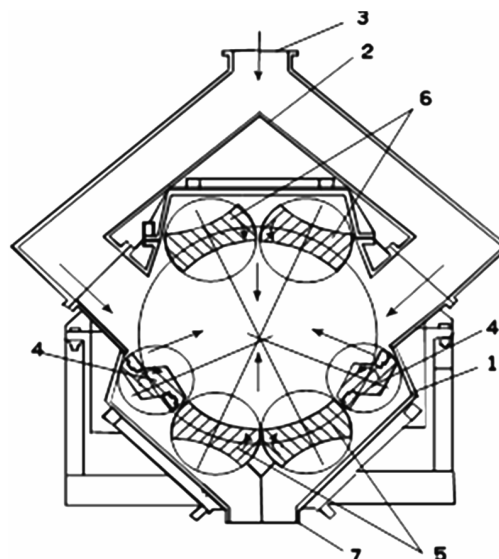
Схематическая конструкция дробилки ДКД-300: 1 – корпус дробилки; 2 – делитель потока; 3 – загрузочный патрубок; 4 – первичные ротора; 5 – нижняя пара роторов; 6 – верхняя пара роторов; 7 – разгрузочный патрубок
